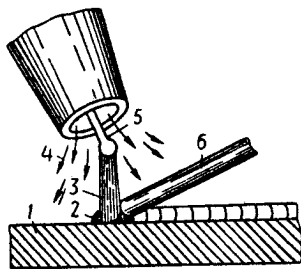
Схема аргонодугового зварювання і наплавлювання нерозплавлюваним вольфрамовим електродом:
